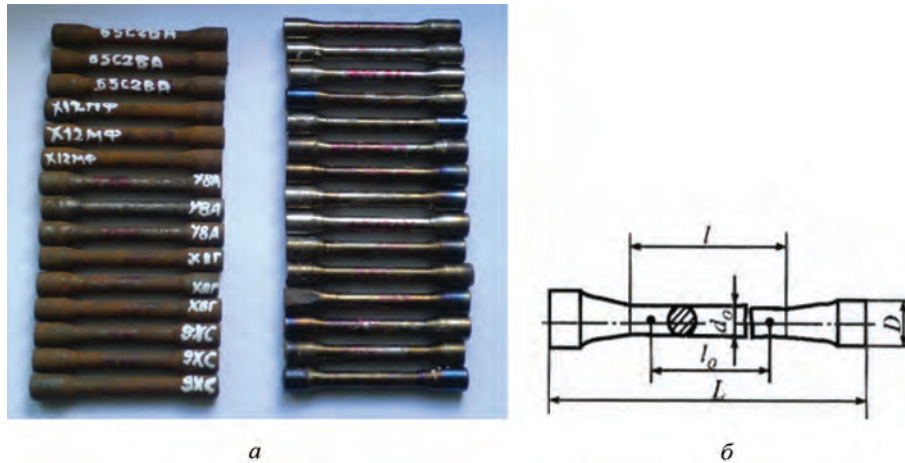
Опытные образцы для испытаний на разрыв: а – общий вид опытных образцов; б – схематическое изображение готового образца
